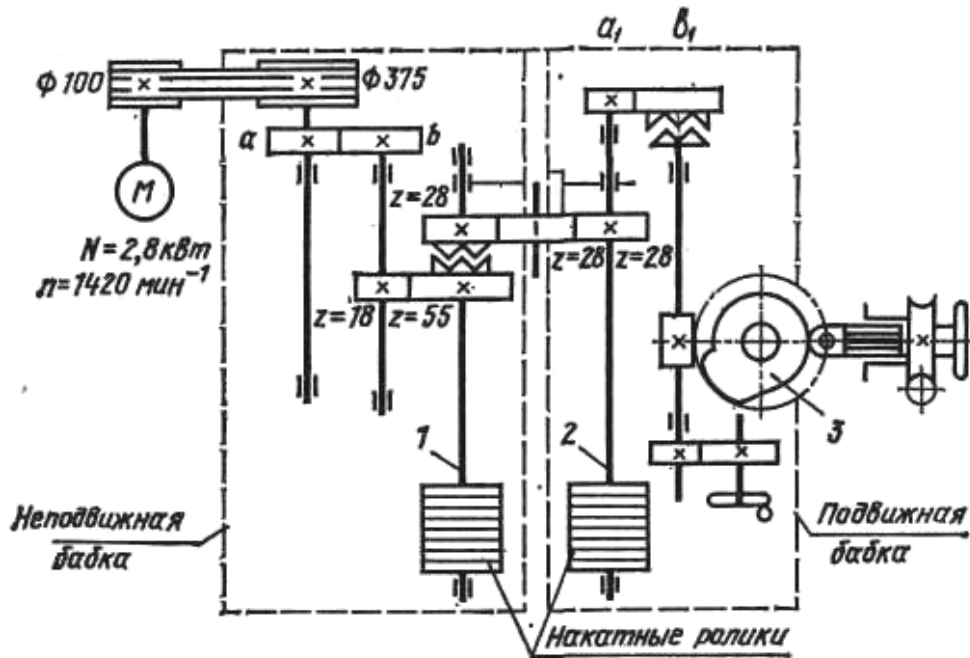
Кинематическая схема резьбонакатного станка модели 5933
